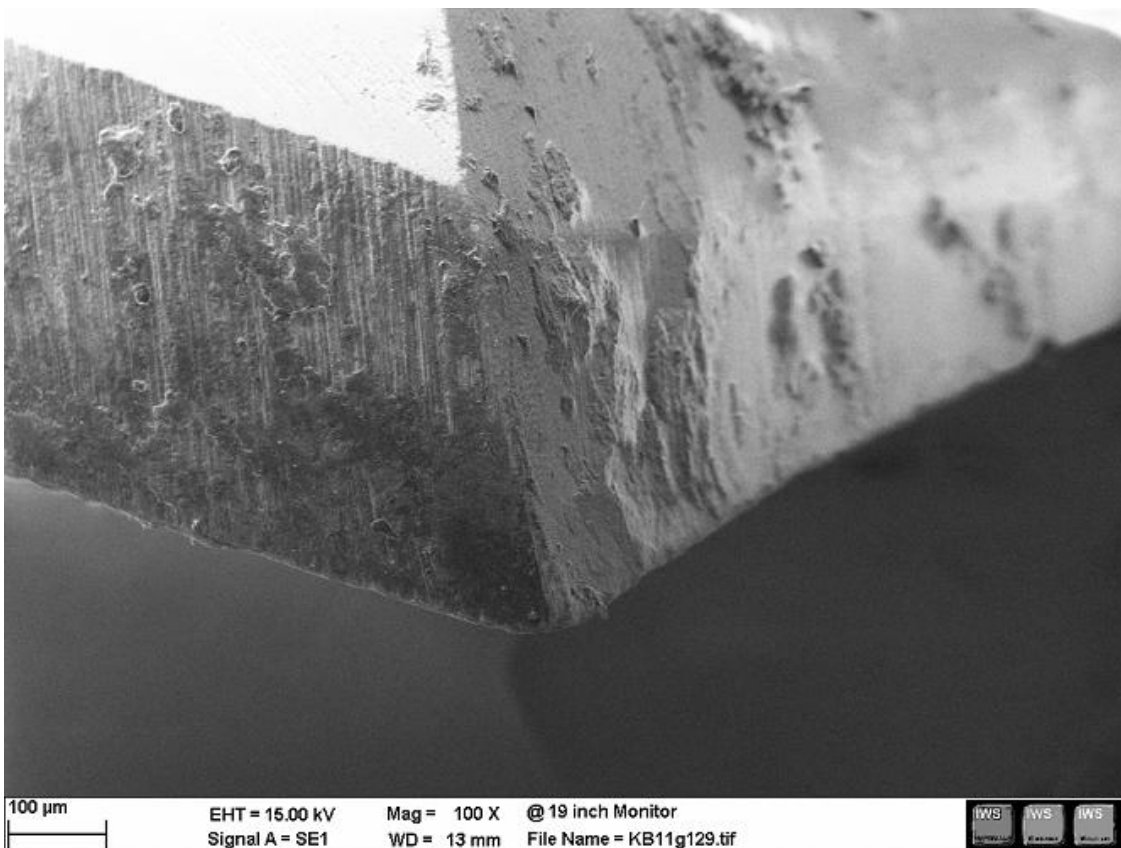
Detail X; Brasseler ZrO₂ CeraDrill; 111 Bohr. Hand; REM (100X)
